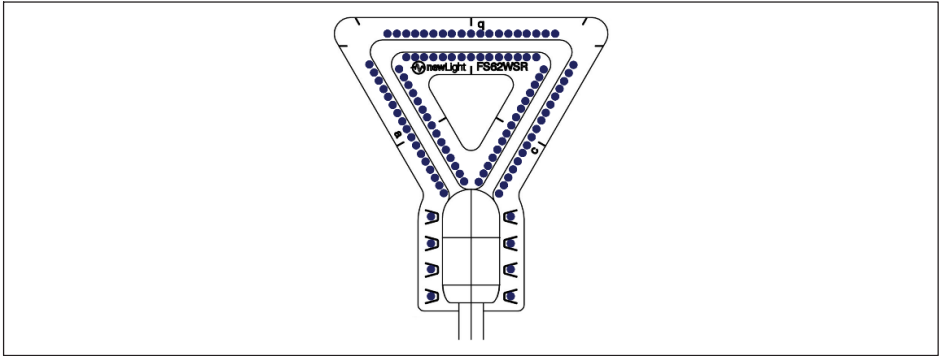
FS62WSR - parcours de soudage 3
